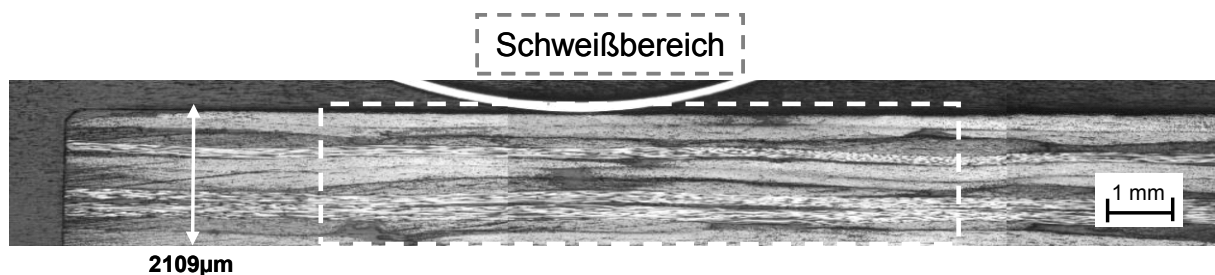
Schliffbild bei Schnitt durch eine Schweißnaht im ausgehärteten Laminat (RTM-Verfahren), Probe 4
